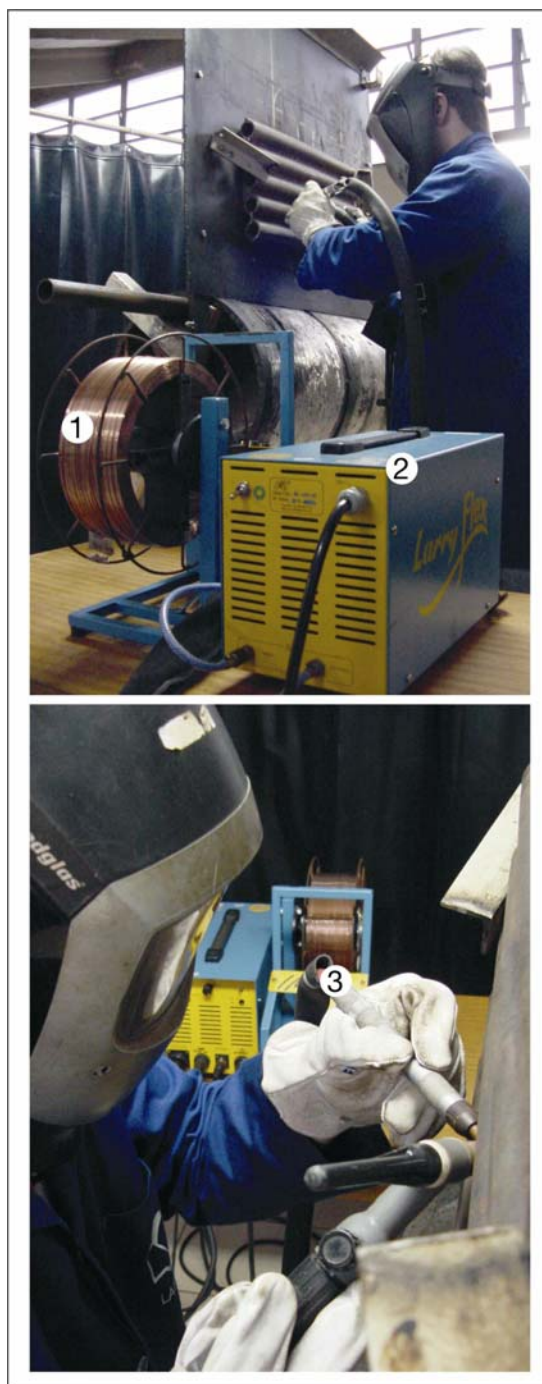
Fonte de soldagem compacta, com sistema inteligente de alimentação de arame contínuo no processo TIG. 1 – cabeçote tracionador de arame, 2 – fonte de soldagem, 3 – Caneta TIG
